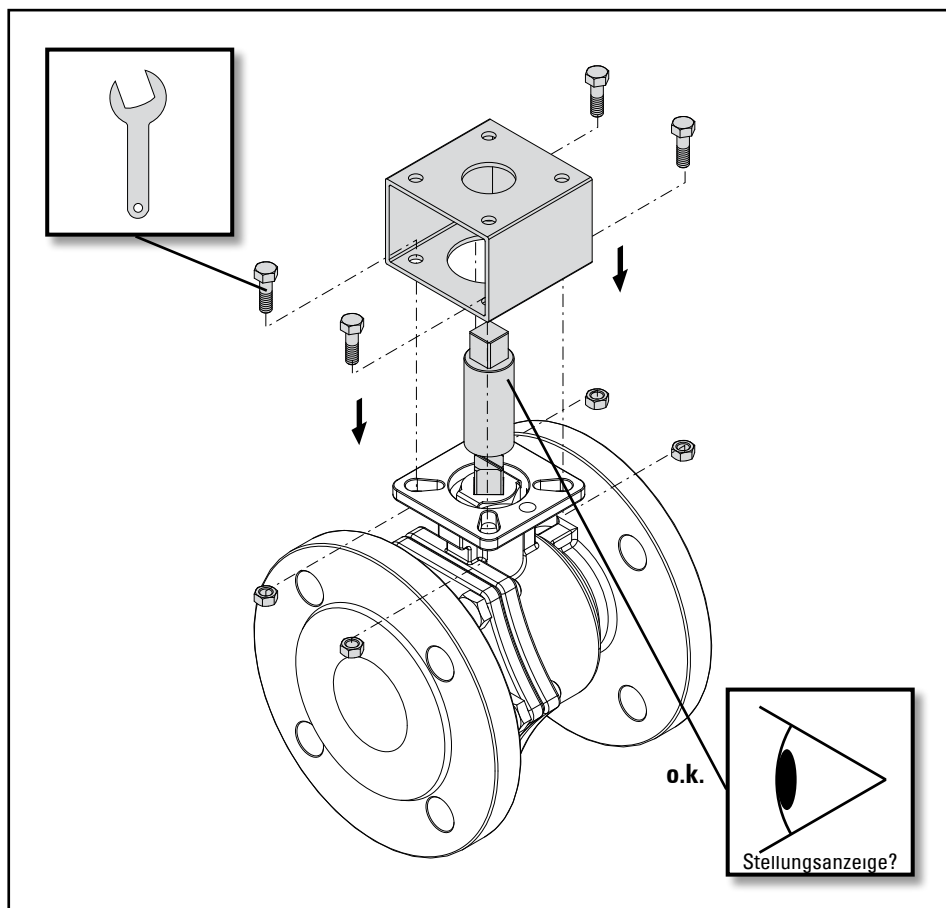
Montage / Demontage, Montage mittels Konsole und Spindel
